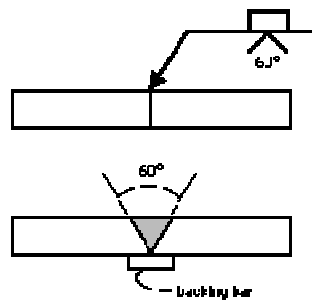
Aplicación de símbolos de soldadura de canal
